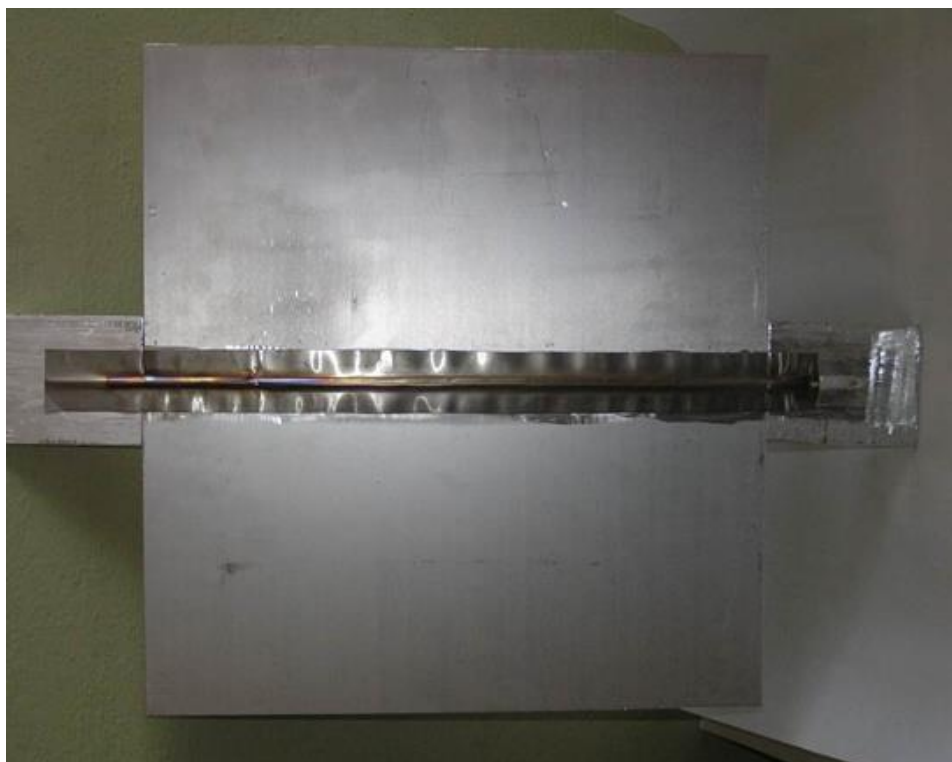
Зовнішній вигляд кореневої частини зварного шва до видалення фольги з нержавіючої сталі (сплав 1570, товщина 6,35 мм, нижнє положення зварювання)
